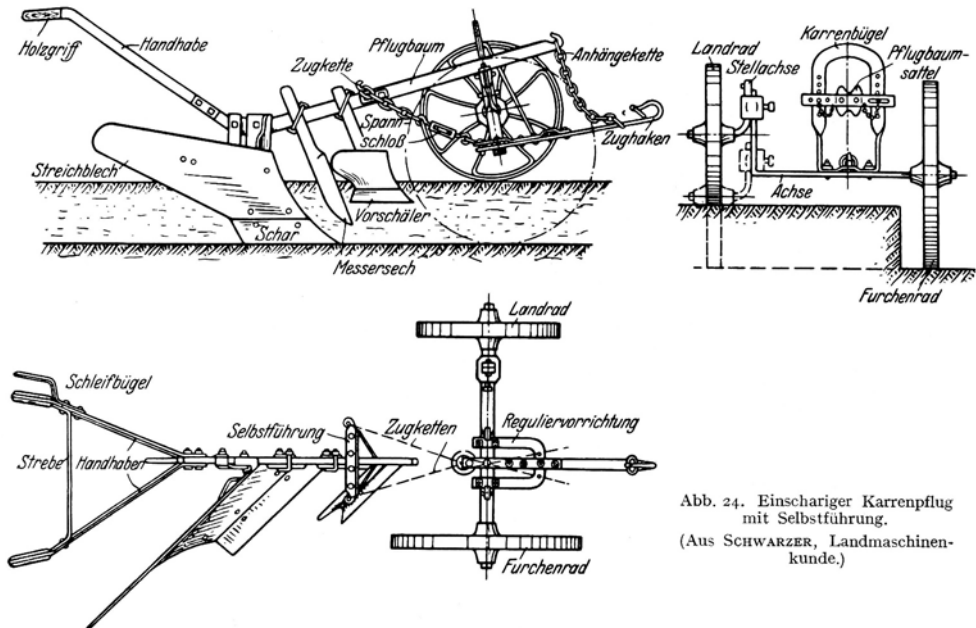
Einschariger Karrenpflug mit Selbstführung.
